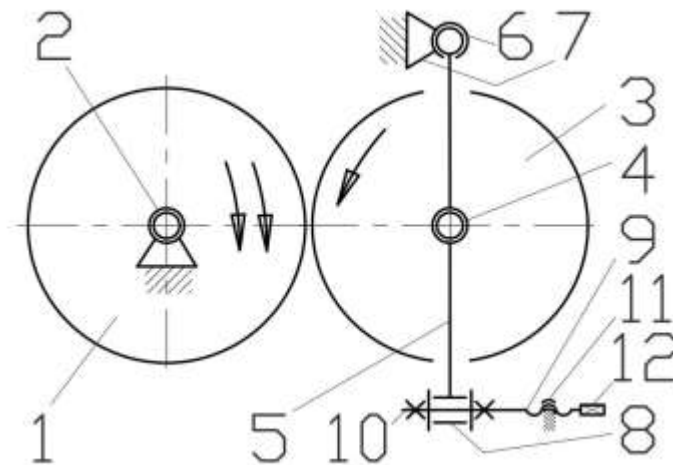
Схема двухвалковой лабораторной дробарки.
